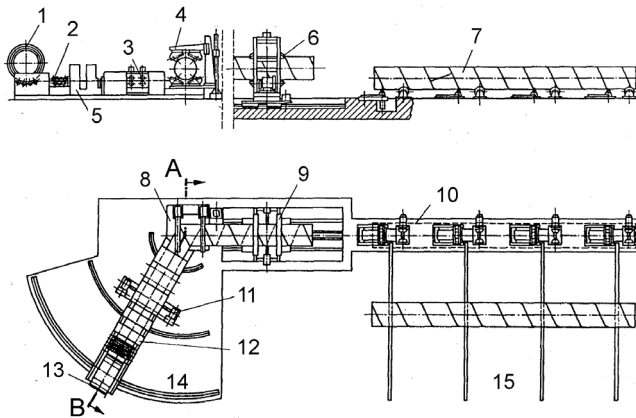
Fertigungsprinzip für Spiralnahtrohre [95]. 1, 13 Ringbund; 2, 14 Richtmaschine; 3, 11 Treibwalzen; 4, 8 Formteil mit Schweißköpfen für Innen- und Außenschweißung; 5, 12 Schopfschere und Stumpfschweißeinrichtung; 6, 9 Rohrtrennvorrichtung; 7 fertiges Rohr; 10 Rollgang mit Auswerfer; 15 Auslaufrost
